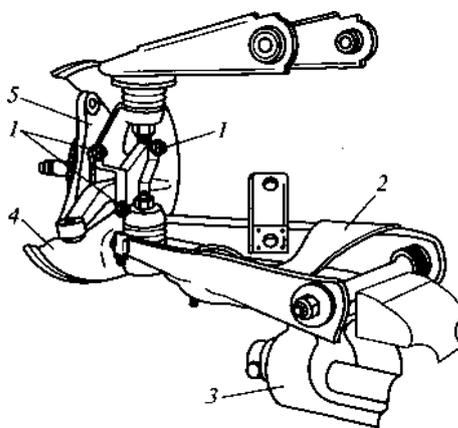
Узел подвески левого колеса, закрепленный на верстаке для разборки:
